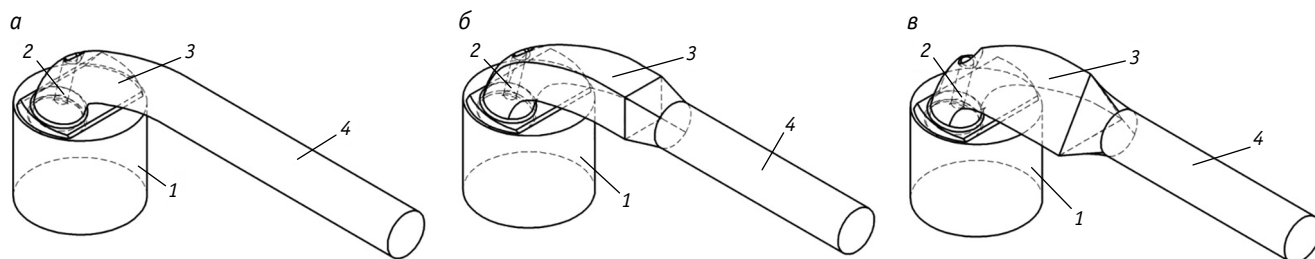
Общий вид исследуемых систем впуска с круглым (а), квадратным (б) и треугольным (в) каналами в ГБЦ: 1 — цилиндр; 2 — клапан; 3 — канал в головке цилиндров; 4 — впускная труба
